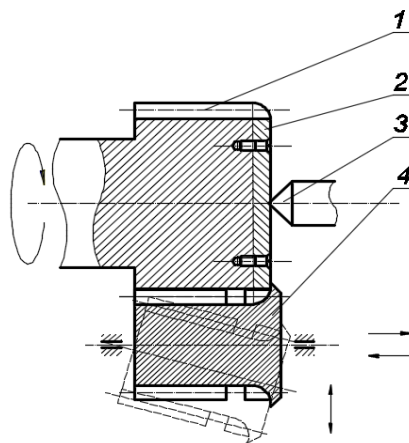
Схема пристосування для випробування накатника для заокруглення торців зубців на бронзових зразках: 1 – синхронізуюча шестерня; 2 – бронзова заготовка
